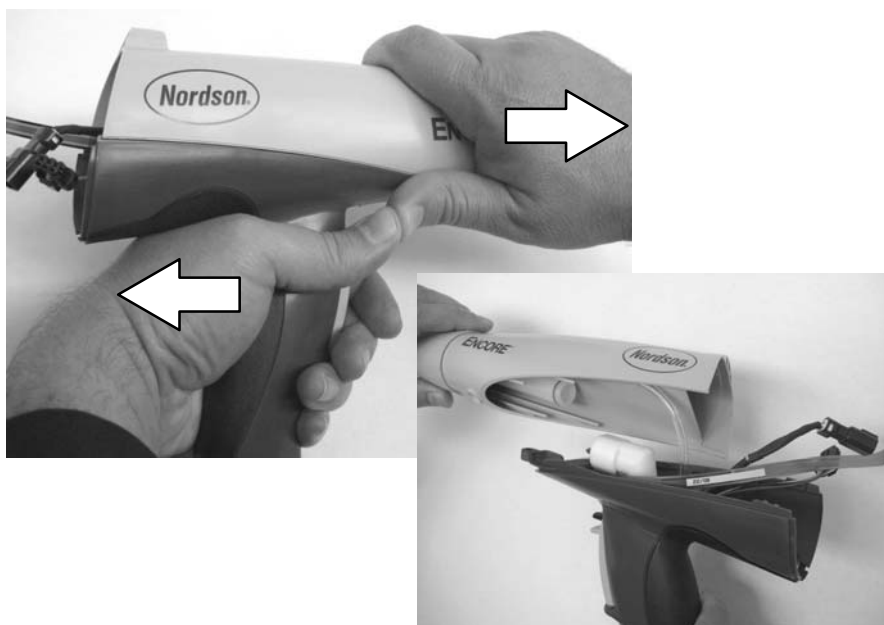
Разъединение рукоятки и корпуса распылителя
